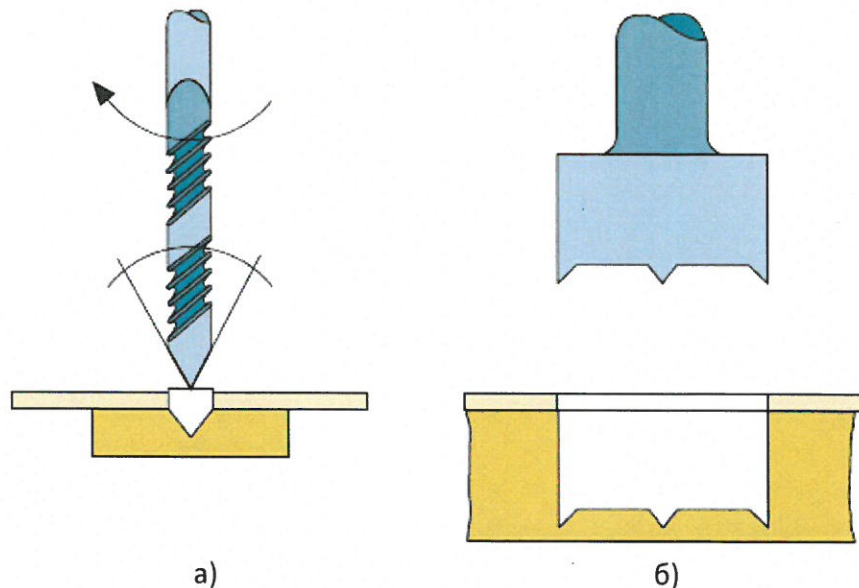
Свердління стільниць: а) за допомогою свердла; б) за допомогою фрези
